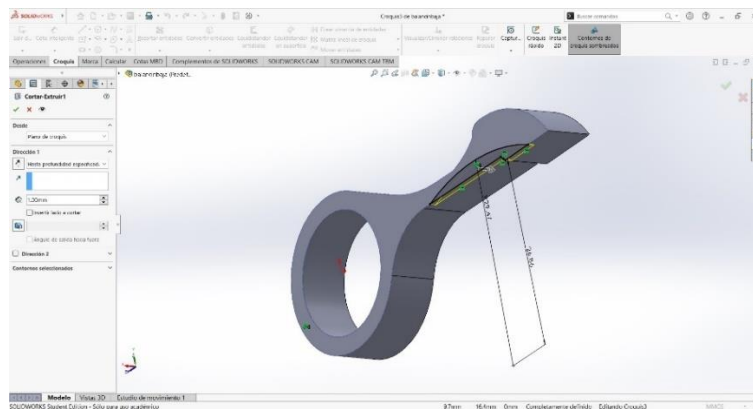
Extrusionado de Recorte en croquis de Balancín 2. Fuente: SolidWorks
